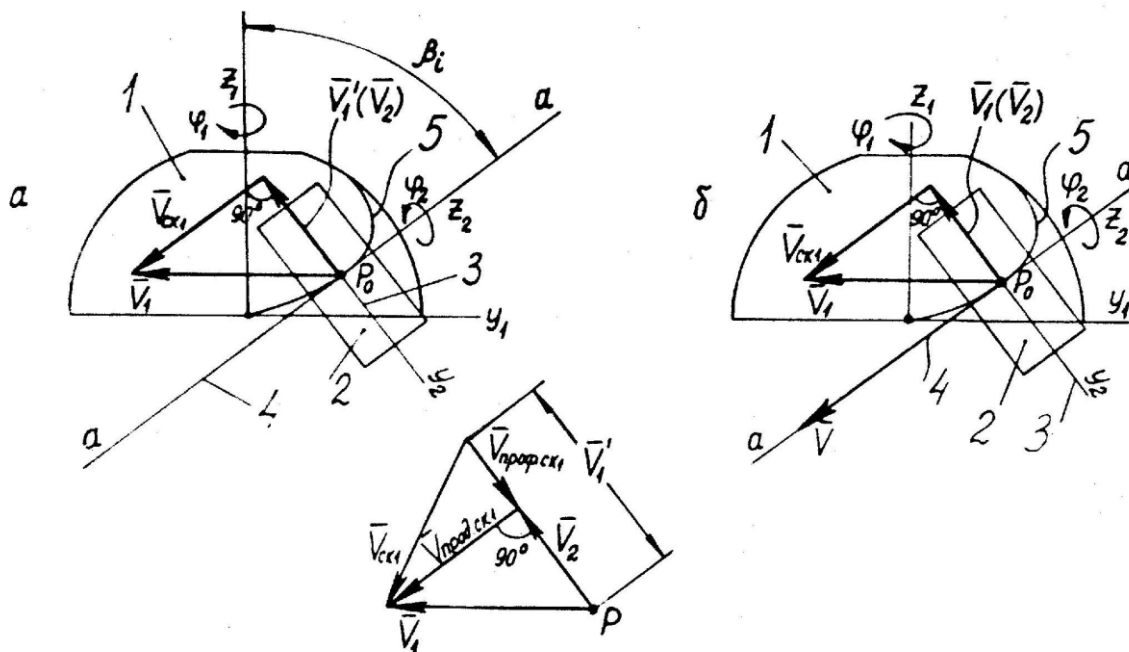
Доказательство наличия скольжения поверхностей зубьев шевера и обрабатываемого сферического колеса:
